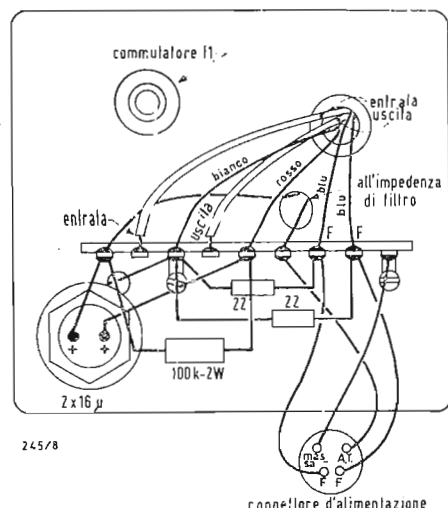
Cablaggio dei componenti disposti sotto la piastrina di supporto.
